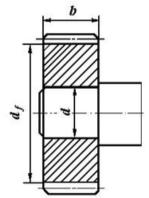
Цилиндрическое соединение вала и шестерни с натягом
